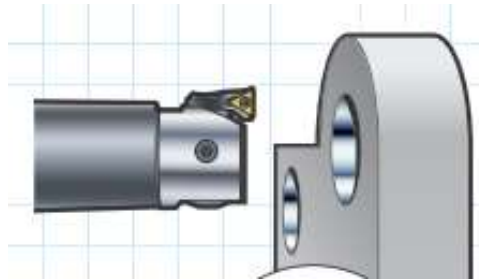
Інструмент для чистової обробки з однією ріжучою кромкою
